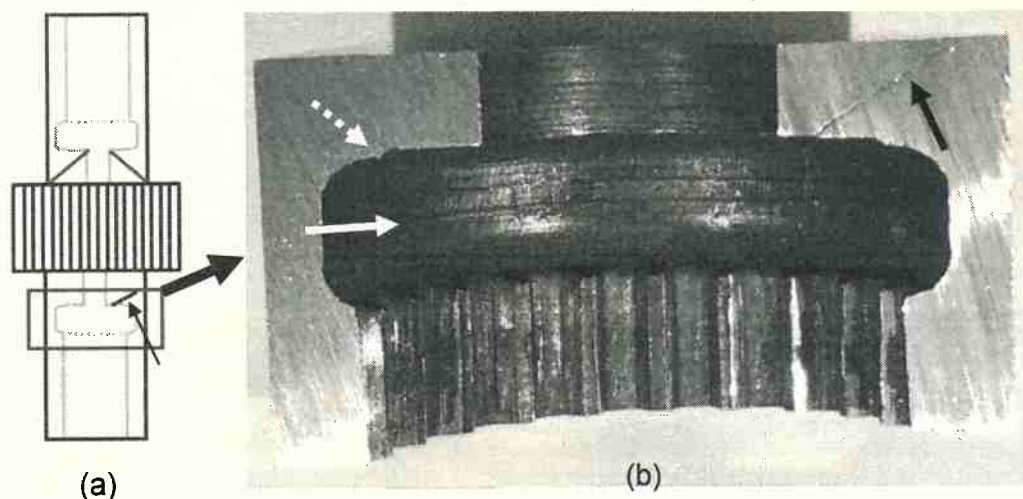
Corte longitudinal do eixo, da Região 3. A seta menor em (a) indica a posição da trinca observada em (b). Seta preta: trinca interna; seta branca: ressaltos de usinagem; seta pontilhada: degrau na superfície de usinagem.
